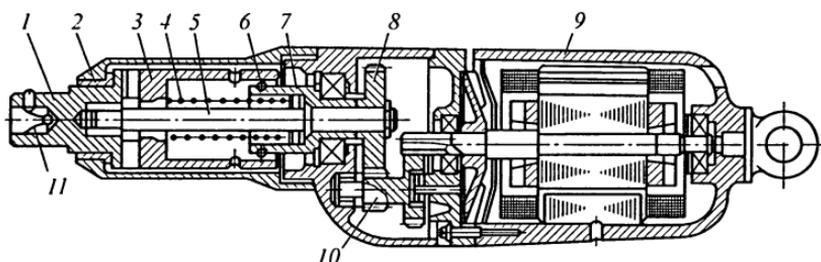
Ударно-импульсный электрогайковерт: 1 — рабочий наконечник; 2 — втулка; 3 — ведомая полумуфта; 4, 11 — пружины; 5 — шпindel; 6 — шарики; 7 — ведущая полумуфта; 8, 10 — зубчатые колеса; 9 — корпус
